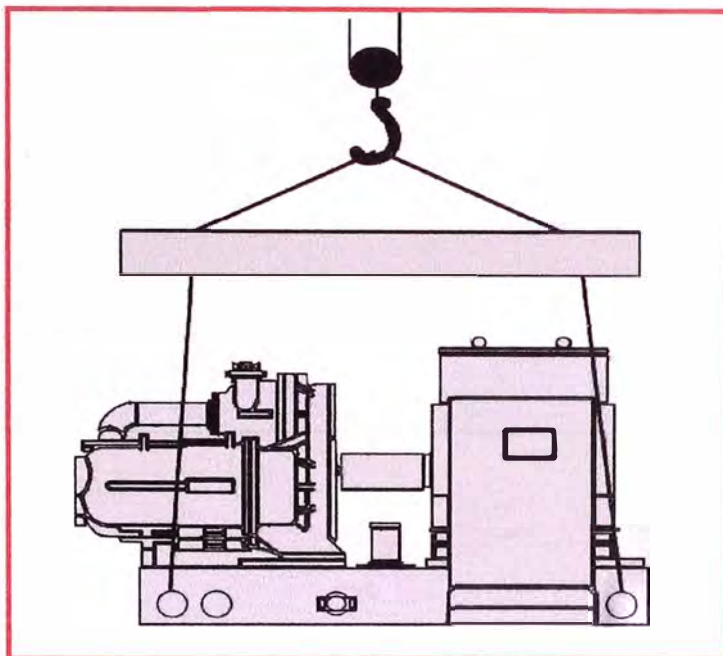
ELEVACIÓN DEL EQUIPO.
